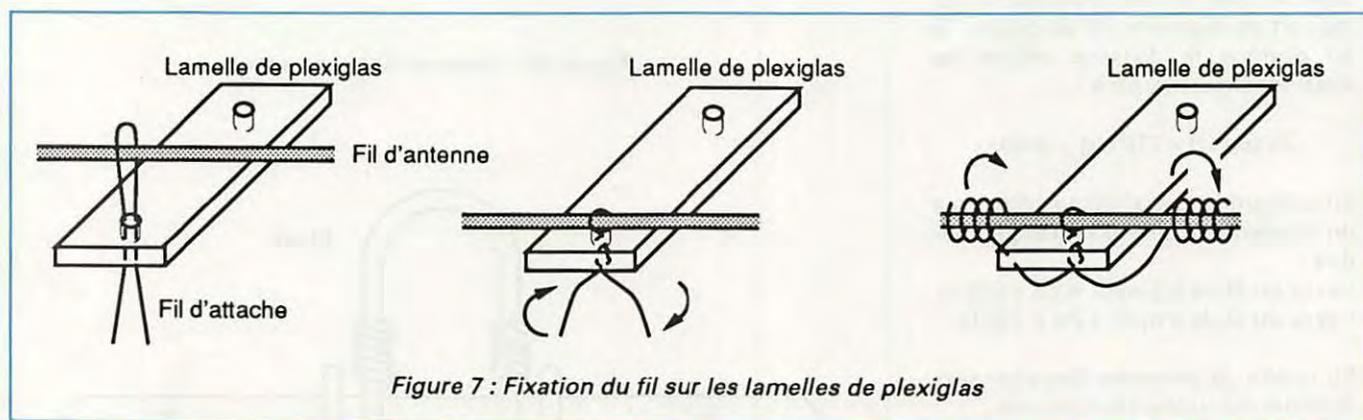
Fixation du fil sur les lamelles de plexiglas
